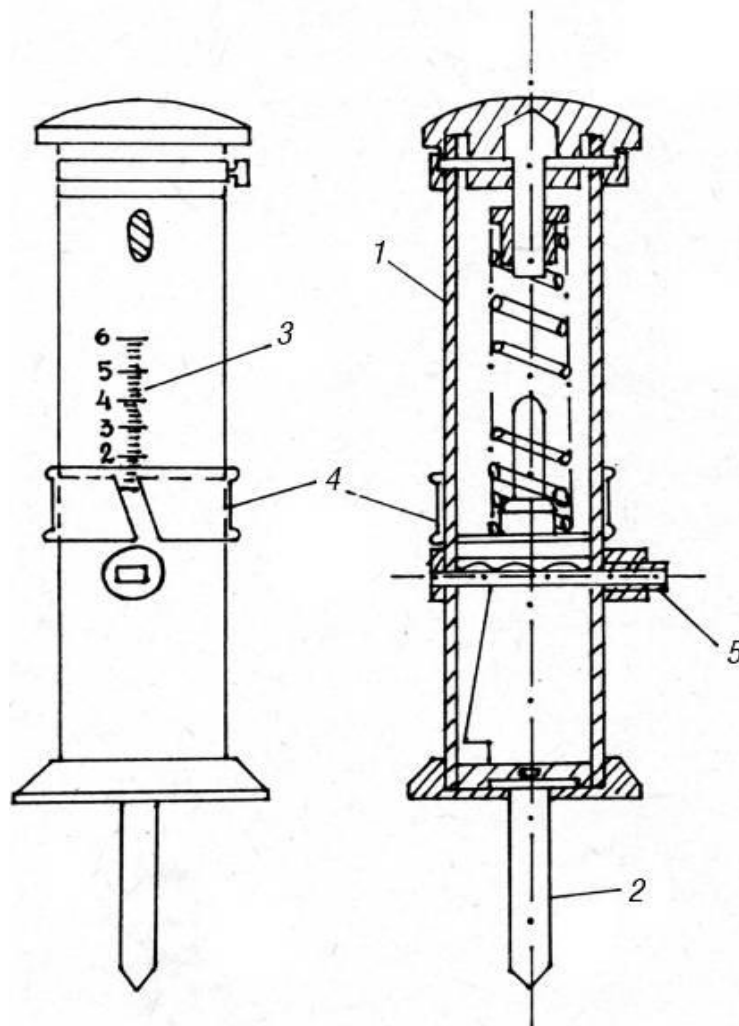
Твердомір конструкції Н.А. Качинського:
